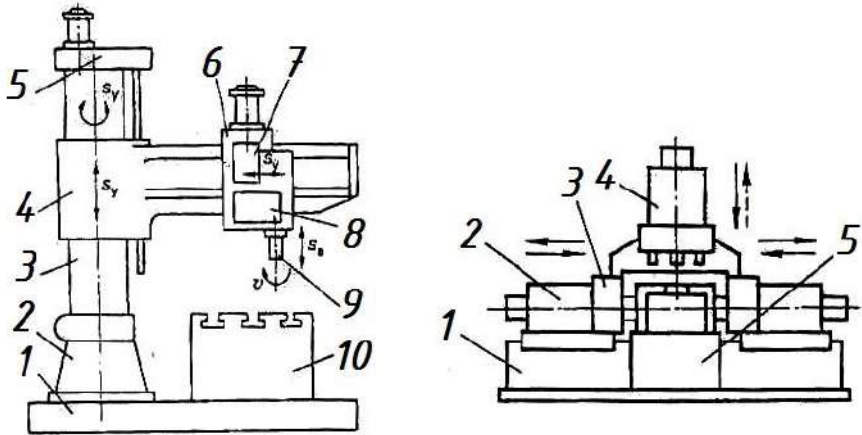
Загальний вигляд радіально-свердлильного верстата та компонування агрегатних верстатів
